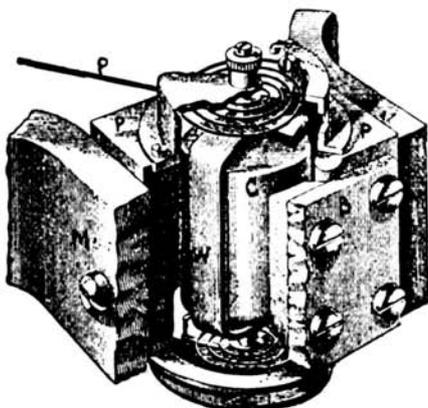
Equipaggio mobile di un milli-amperometro.
